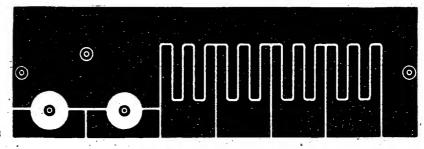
Deska s plošnými spoji S79 modulu elektromotorků (vhodné rozmístění součástek viz obr. 3)
